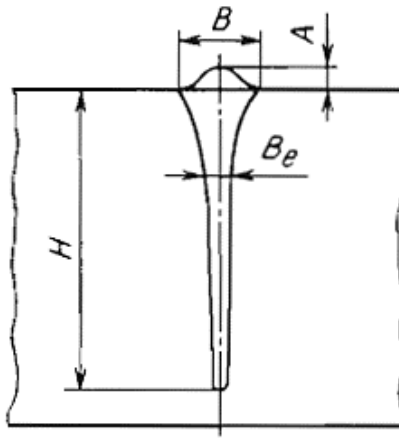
Характерная форма поперечного сечения сварного шва при электронно-лучевой сварке:
